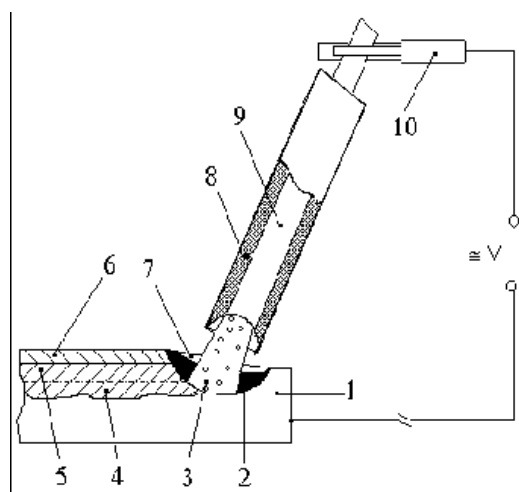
Схема процесса ручной дуговой сварки
